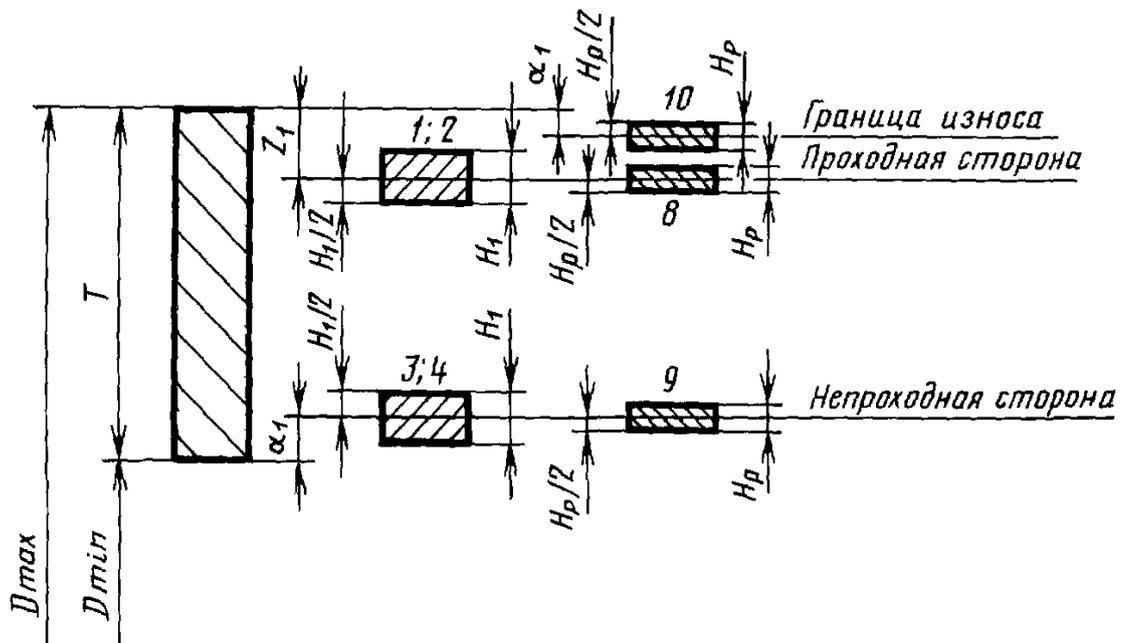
Схема расположения полей допусков калибра-скобы
